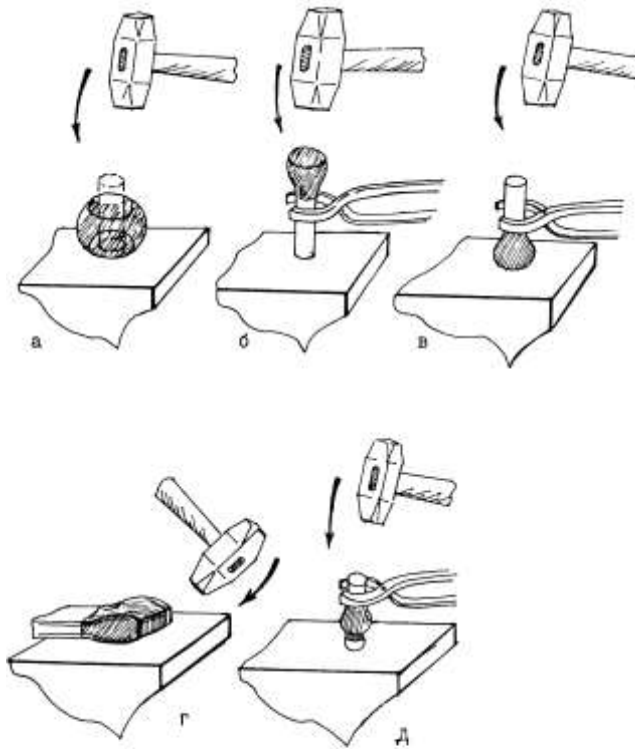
Ковальська обробка металу (з'єднання стійок із тягами)
